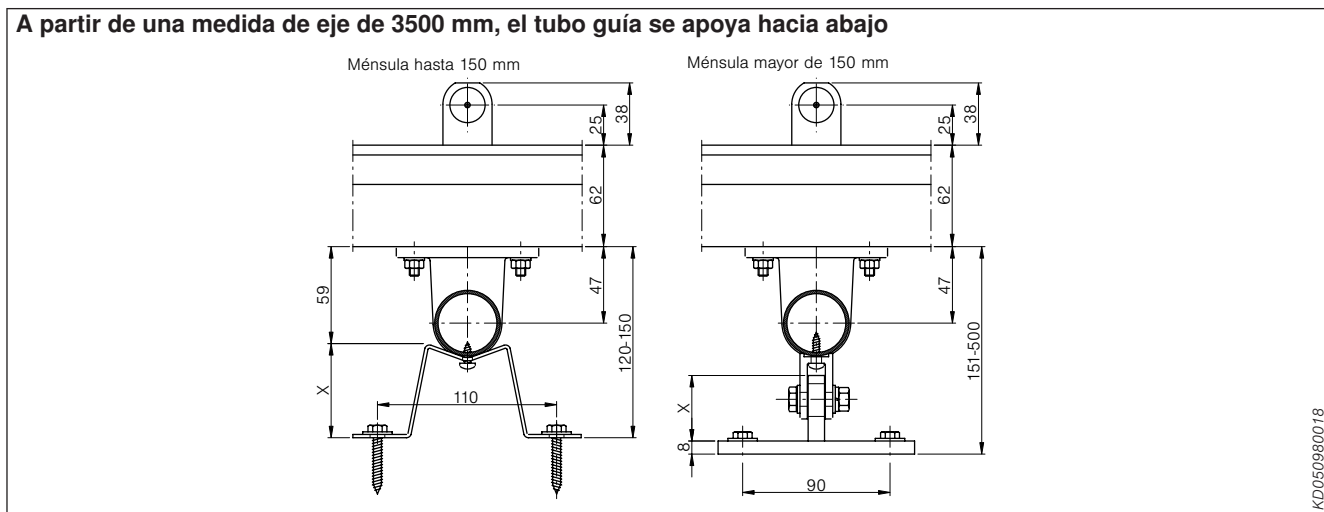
Apoyo del tubo guía a partir de 3500 mm de medida del eje
